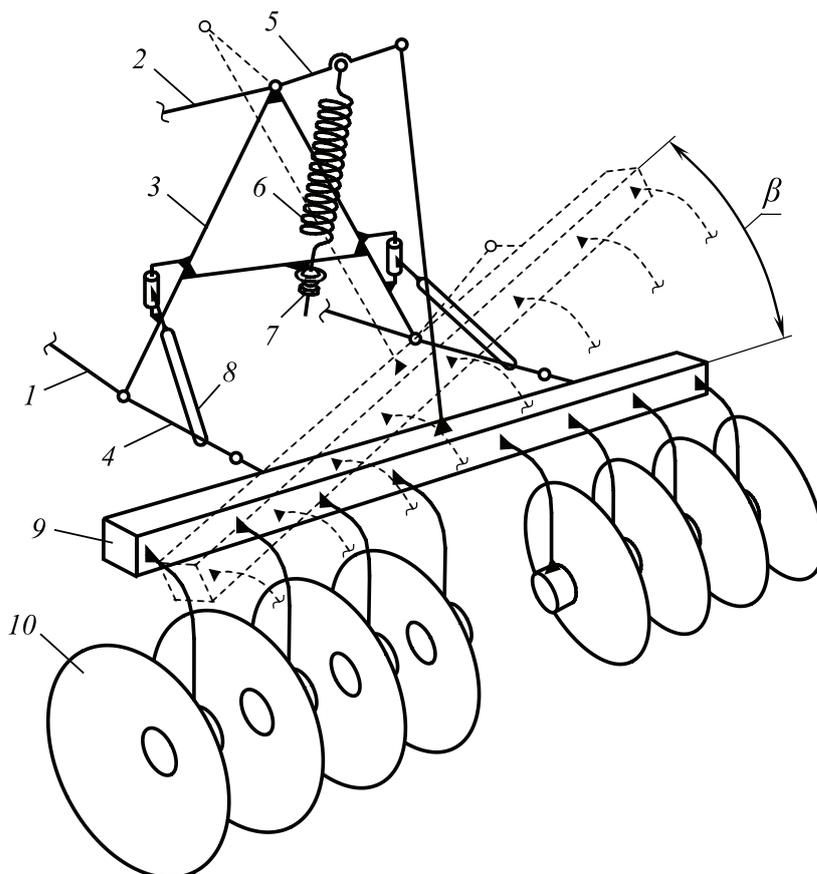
Общий вид и устройство дискового культиватора с приспособлением к навесному устройству трактора:
